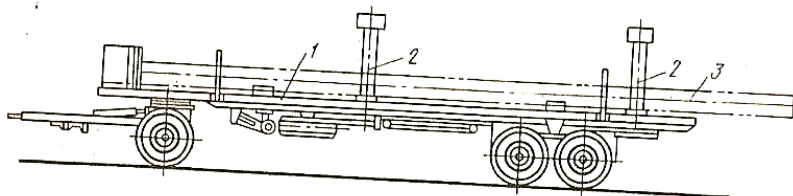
Платформа для перевозки железобетонных стоек опор: 1 рама; 2 гидрокран; 3 – стойка.
